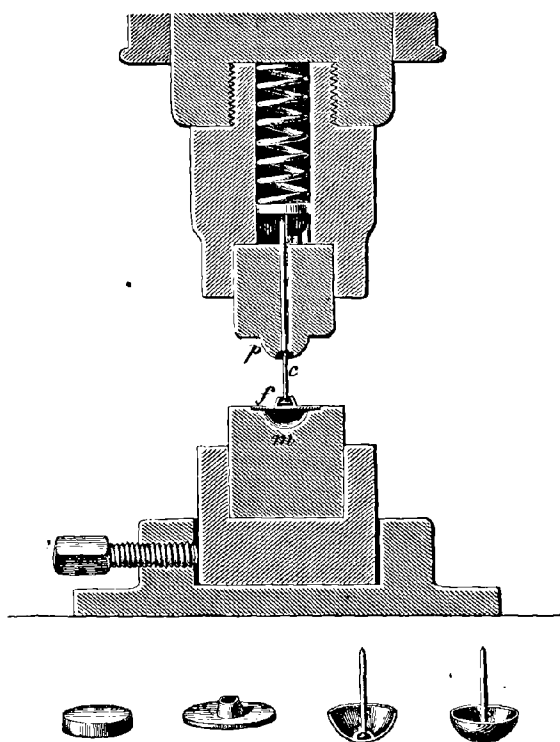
Flan. Flan étampé. Clou fabriqué.
